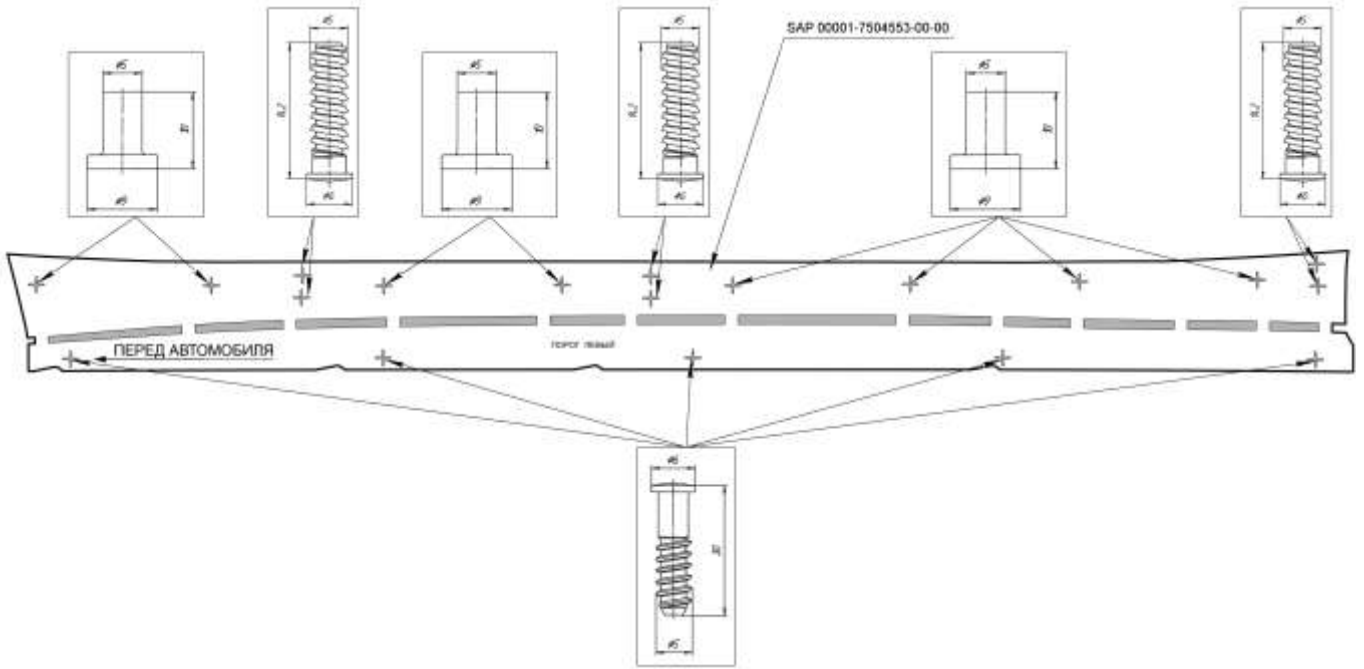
Схема разметки точек приварки шпилек по приспособлению.
